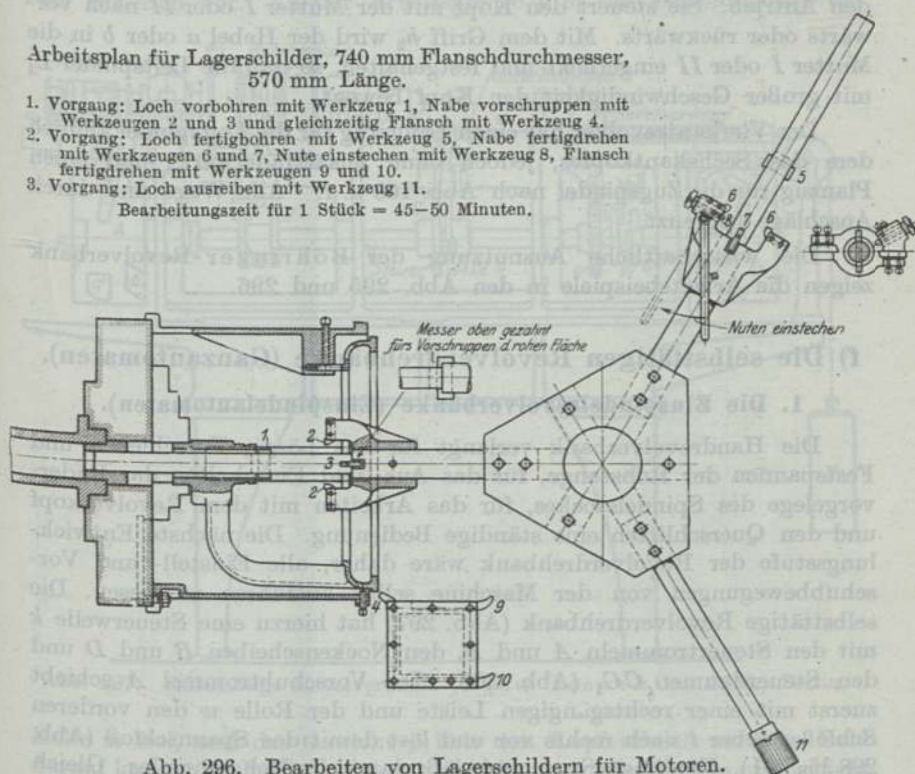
Bearbeiten von Lagerschildern für Motoren.
